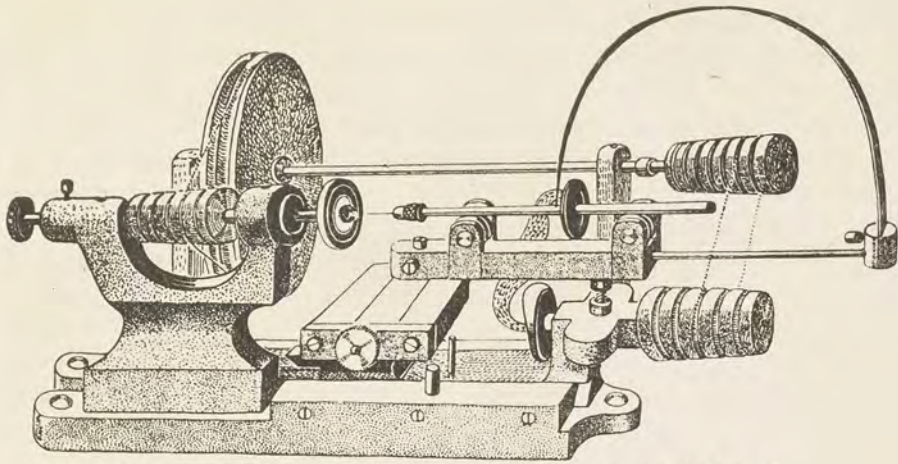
Maschine zum Ausschleifen der Bohrung des Ziehsteins.
